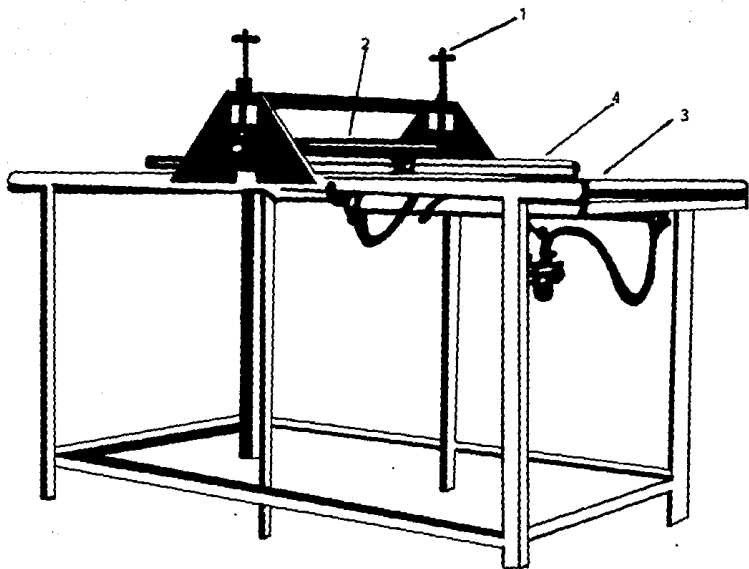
TROQUEL ACERO. 1.- Manivela para ajustar presión del rodillo. 2.- Rodillo. 3.- Plancha. 4.- Molde.
